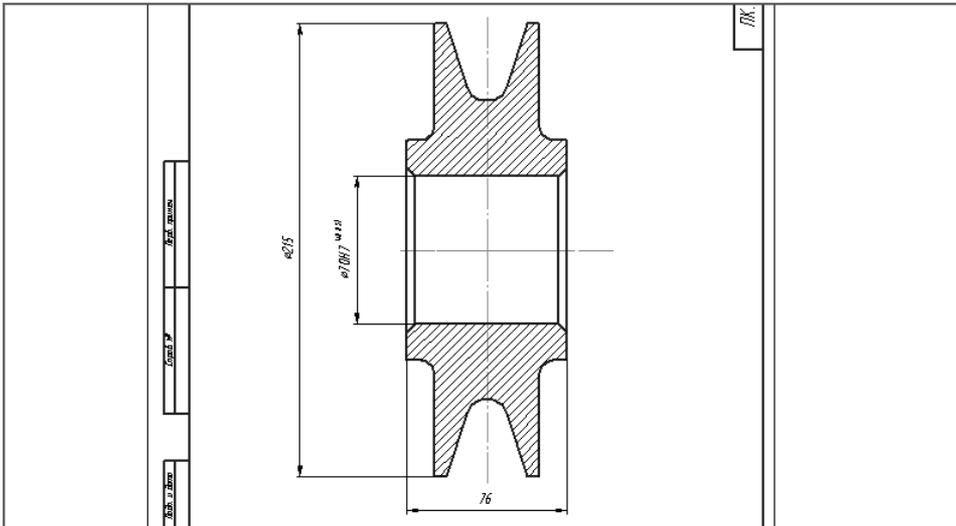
Представление Ролика с удаленными лишними размерами и обозначениями шероховатости
